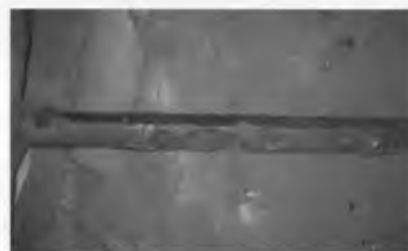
Внешний вид проходного сифона С70-200 (трубка пролетная) марки МКС-72 после разливки стали ШХ15
